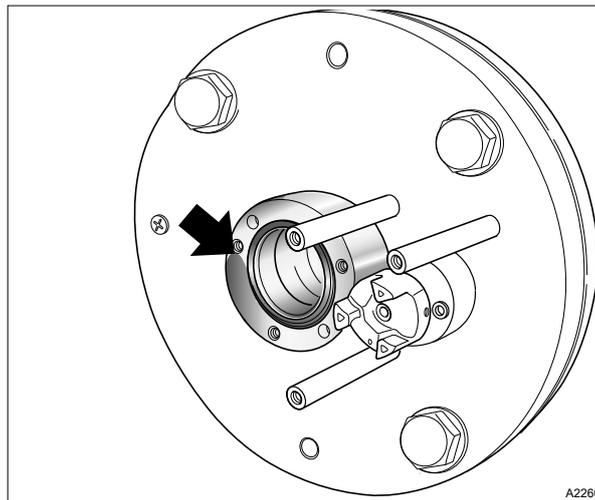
Support (flèche) du tube de protection de la lampe UV
